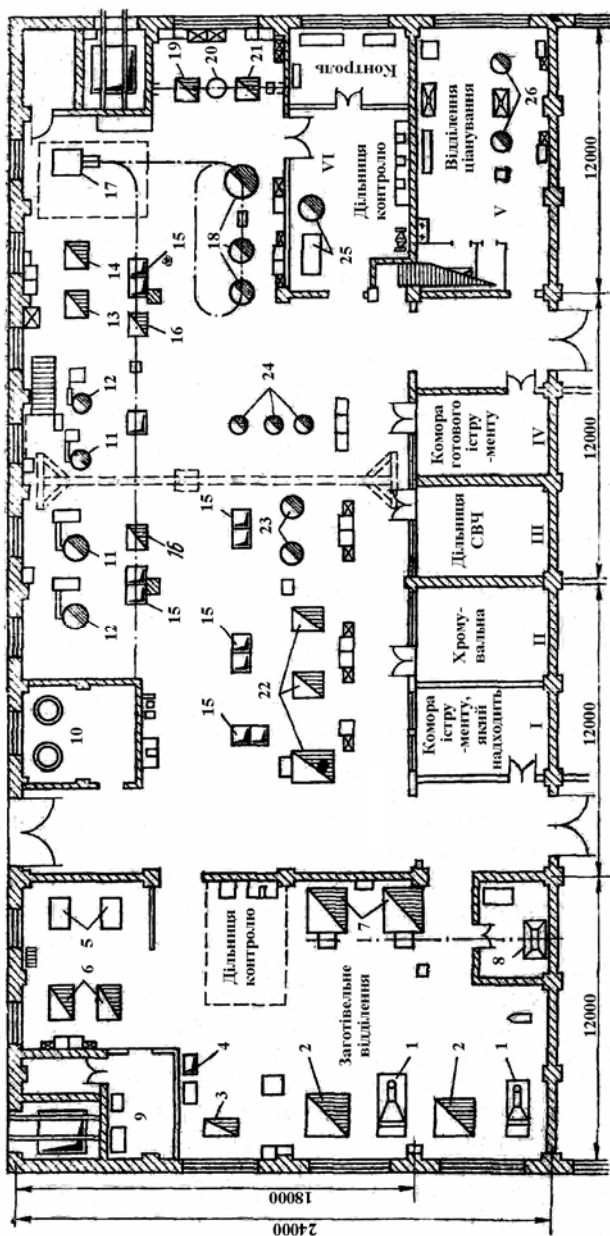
Плани універсального термічного відділення для обробки інструменту:
